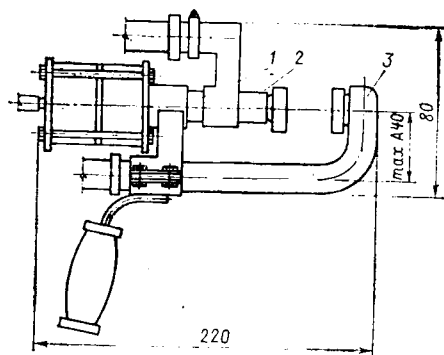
Сварочные клещи Тюменского ДСК для сборки каркасов на вертикальных установках
